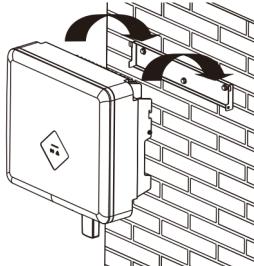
Montaggio dell'inverter sulla staffa da parete
